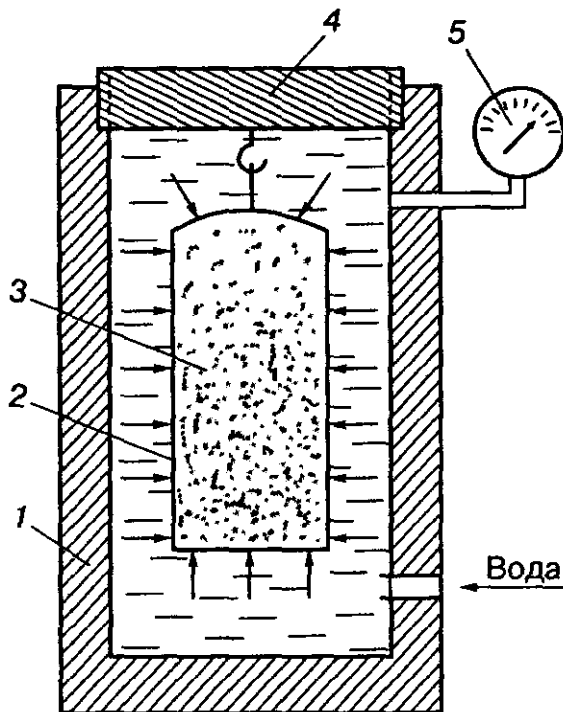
Схема установки для гідростатичного пресування порошків [1]:
